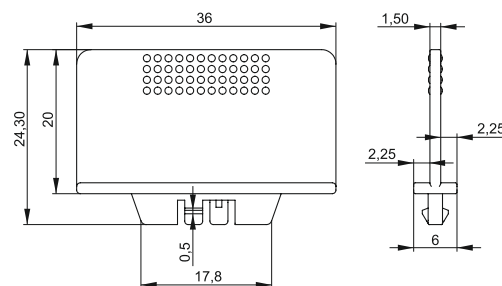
Габаритные размеры перегородки / Figure 3 – Overall dimensions of the separating partition
